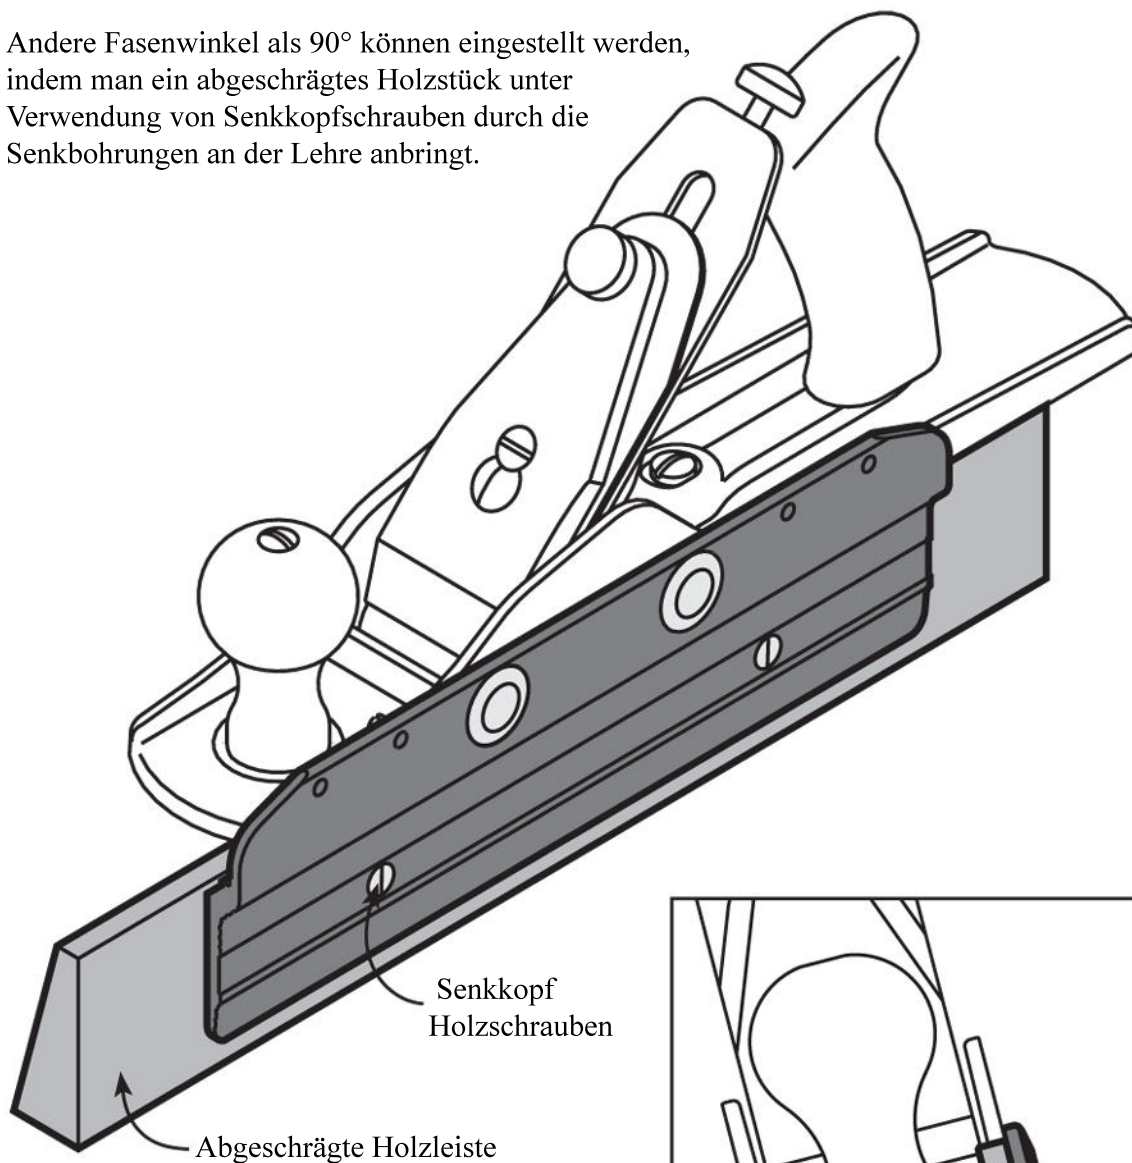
Anbringen eines abgeschrägten Holzstücks an der Innenfläche der Lehre, um abgeschrägte Kanten abzurichten
